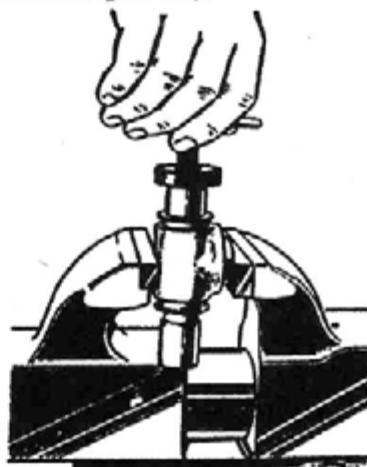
Извлечение пружинного кольца автоматического устройства из колесного цилиндра
